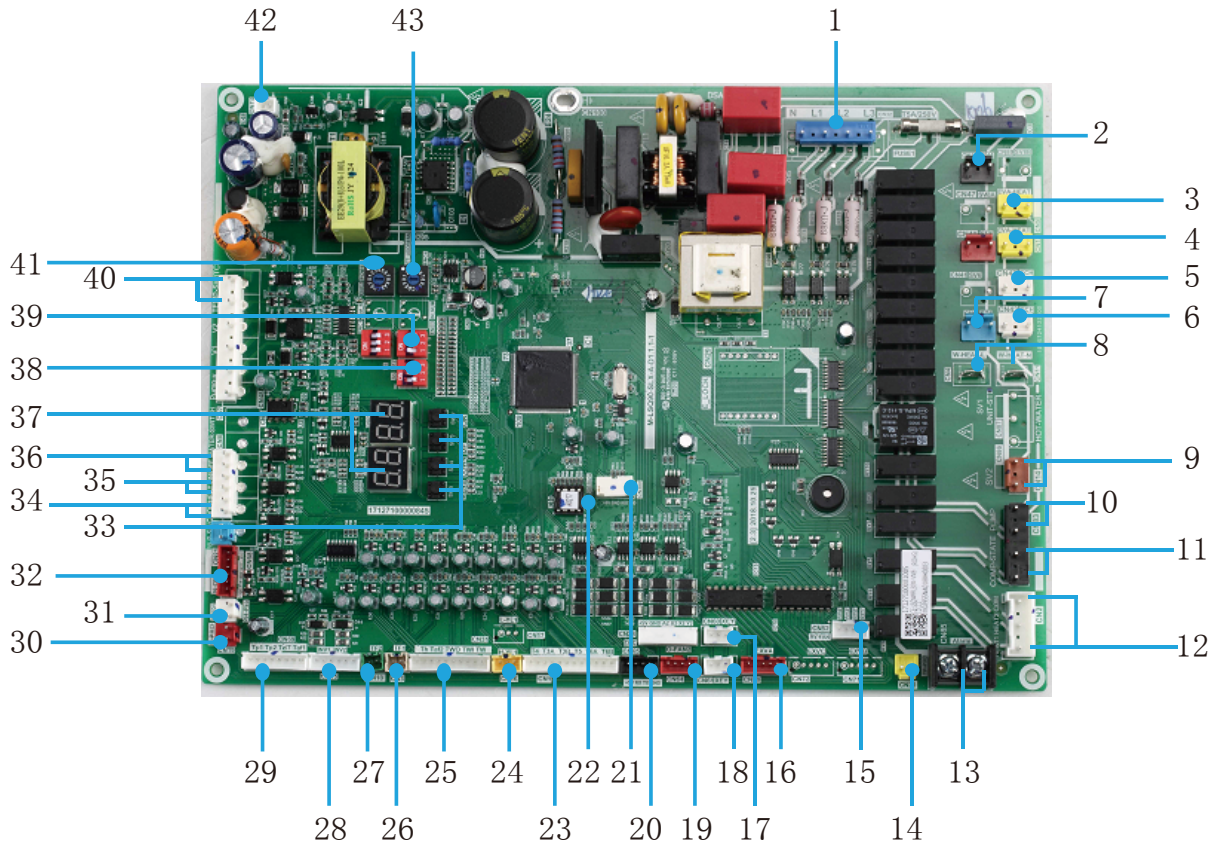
PCB principal do KEM-30 DRS4.1 e do KEM-60 DRS4.1
